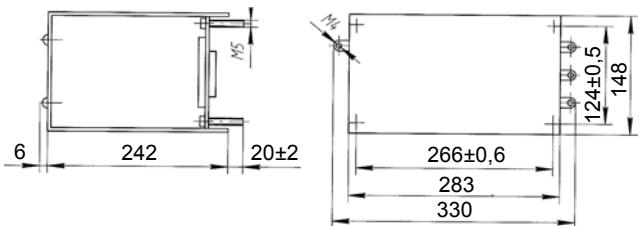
Габаритные, установочные размеры блока типа БЭ 1105.
